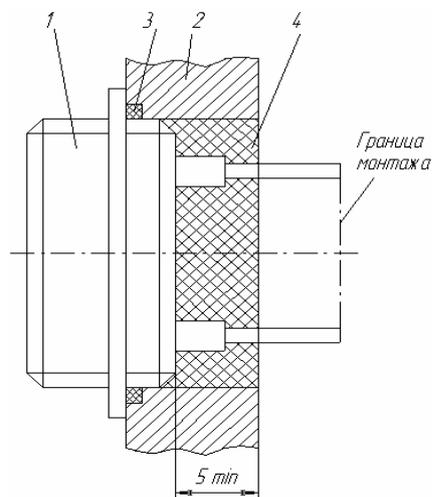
Герметизация вилки разъёма РСГ с помощью уплотнительной прокладки и компаунда: 1 – вилка разъёма; 2 – корпус блока; 3 – уплотнительная прокладка; 4 – компаунд
